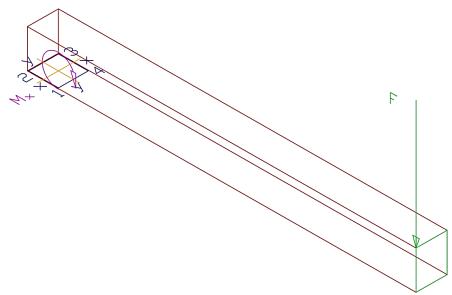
Diagrama de fuerzas que actúan sobre cordón de soldadura
